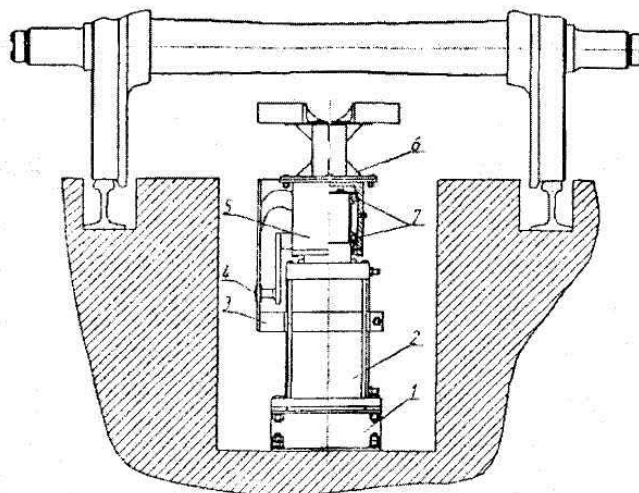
Общий вид установки: 1-рама; 2-пневмоцилиндр; 3-направляющая пластина; 4-колесо; 5-поворотное устройство; 6-опорная крестовина; 7- подшипники.
